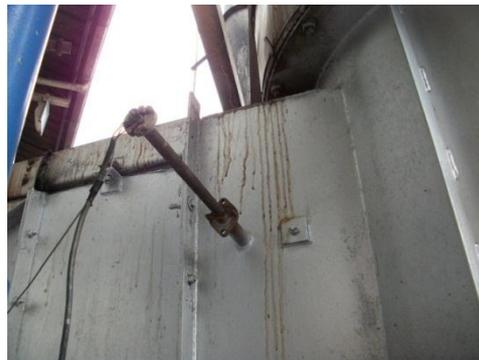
Termocuplas en el Horno de Fundición de Aluminio
